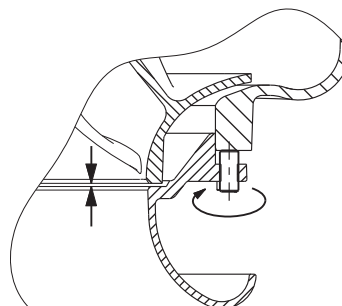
Осевой зазор рабочего колеса, типы установок S, C и ST
